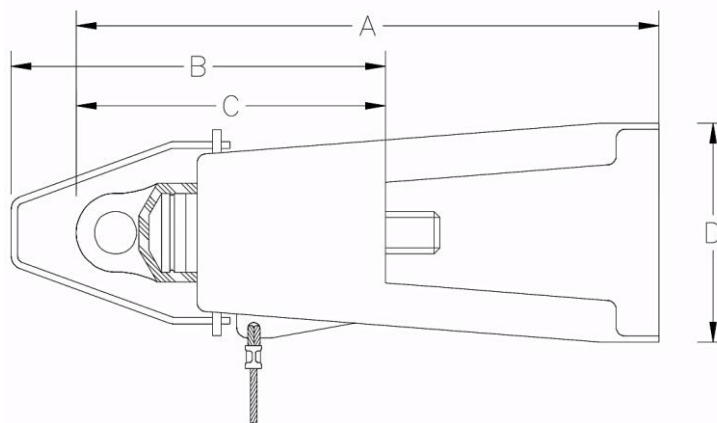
Dimensiones de tapón aislado 600 A, [12].
